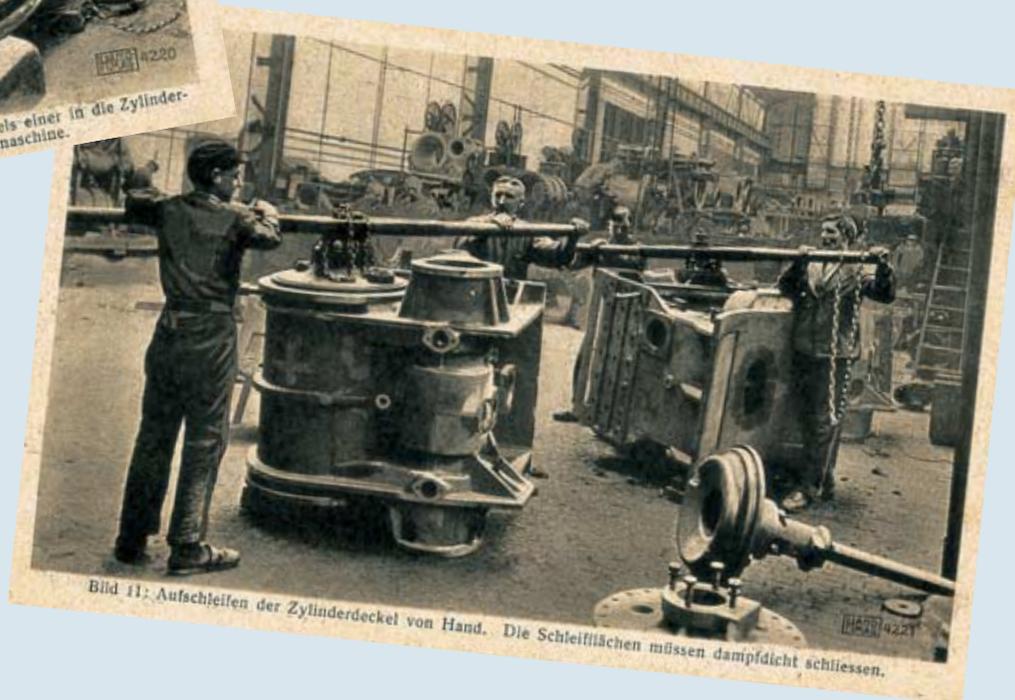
Aufschleifen der Zylinderdeckel von Hand. Die Schleifflächen müssen dampfdicht schliessen.
